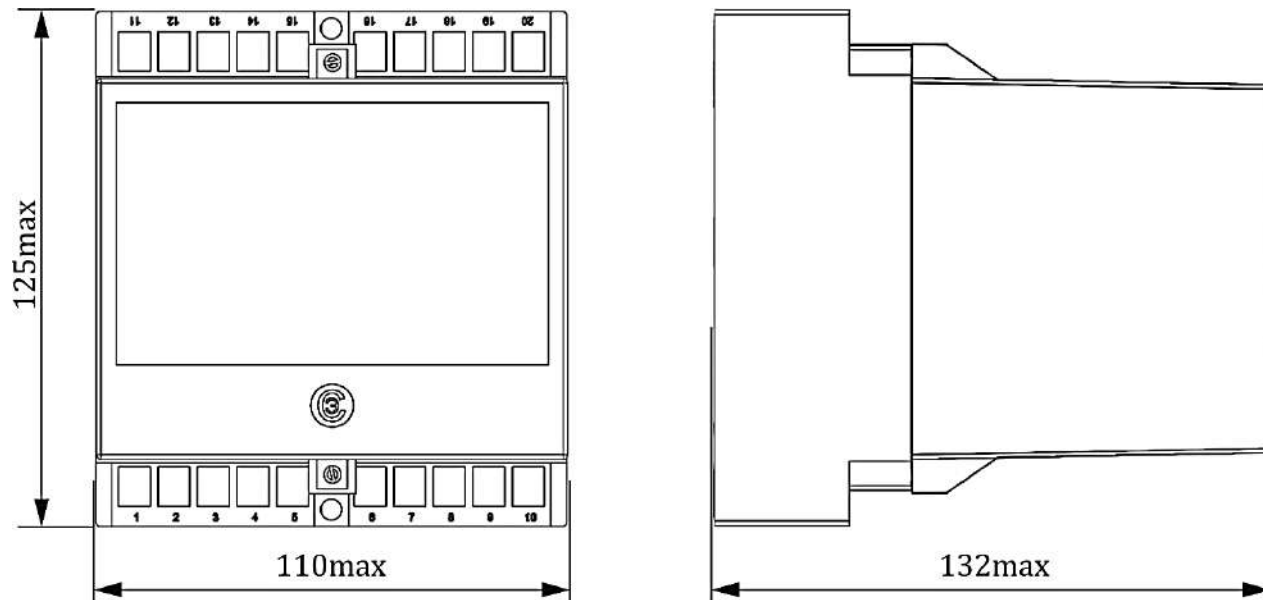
Габаритные и установочные размеры корпуса EB20
